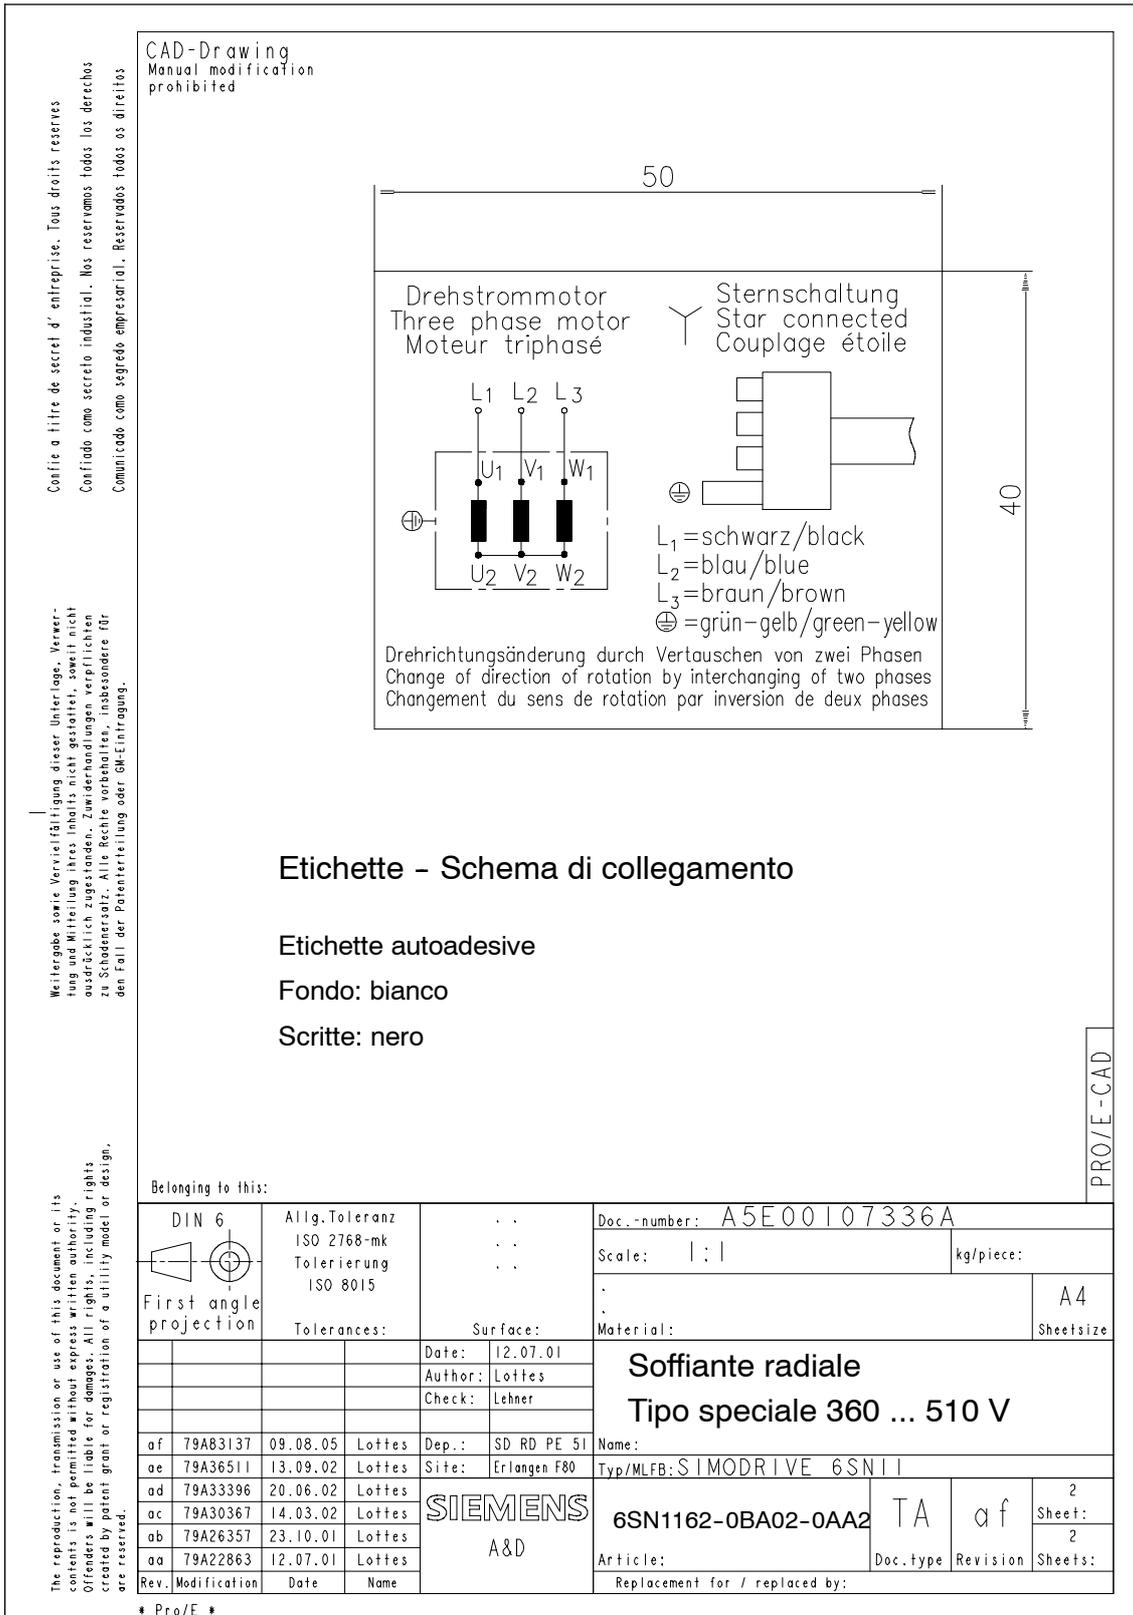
Ventilatore montato, 6SN1162-0BA02-0AA2; schema di collegamento
